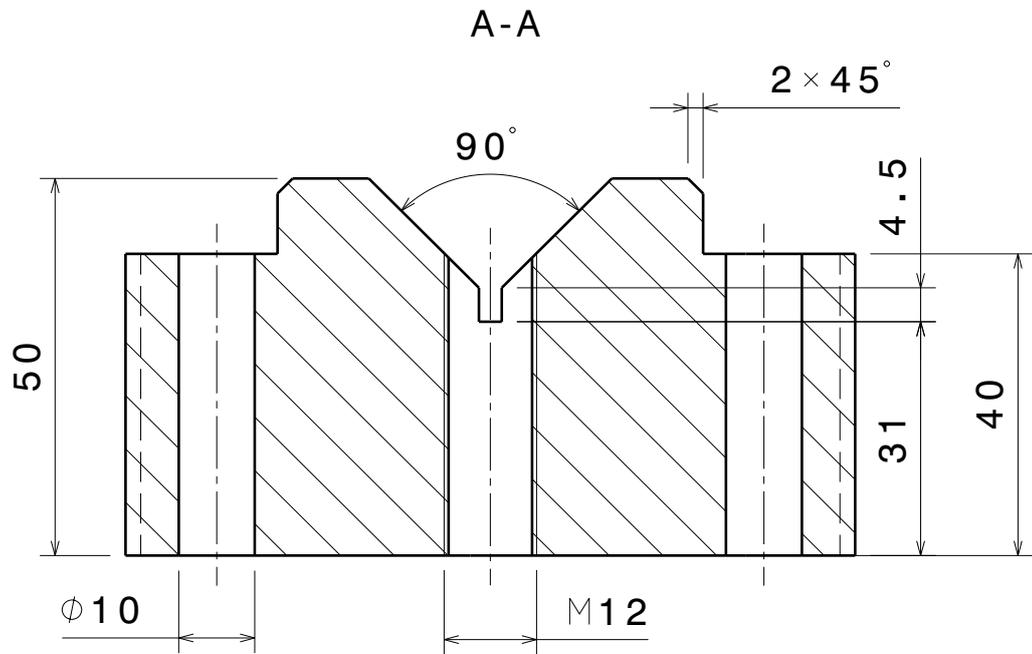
Assembly Design final de l'ensemble Vé réglable [1], [2]
